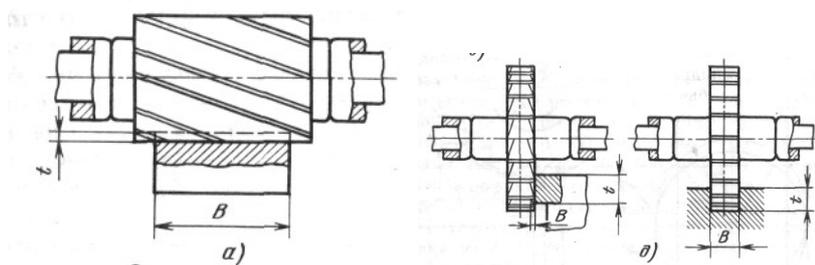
Типы фрез и обрабатываемых поверхностей
